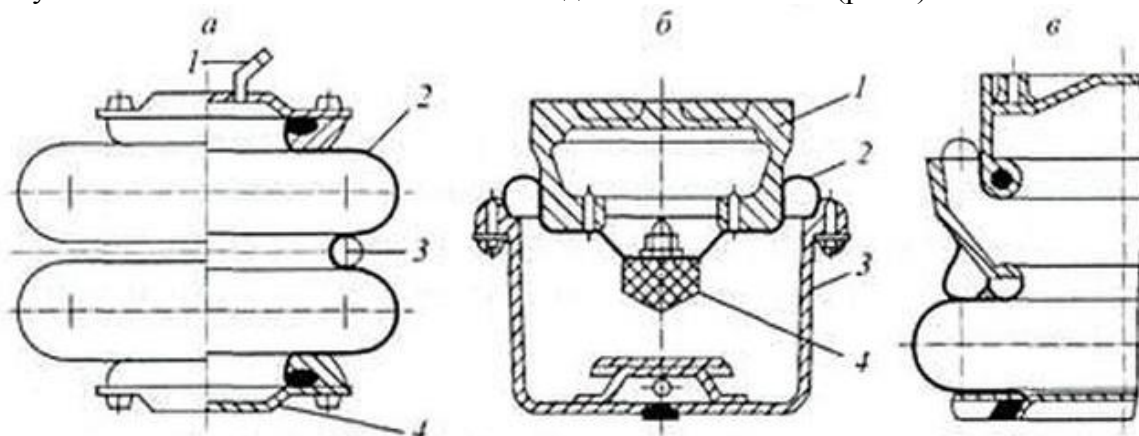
Пневматические рессоры типов: а - баллонного: 1 - патрубок для подвода воздуха; 2 – резино-кордная оболочка; 3 – опоясывающее кольцо; 4 – нижняя опора; б – диафрагменного: 1 – надрессорная балка; 2 – диафрагма; 3 – корпус; 4 – ограничитель; в – смешанного типа. Данные изменения конструкции уменьшают акустическое гудение в салоне вагона, а также обеспечат снижения шумовых и вибрационных показателей более чем в два раза.
